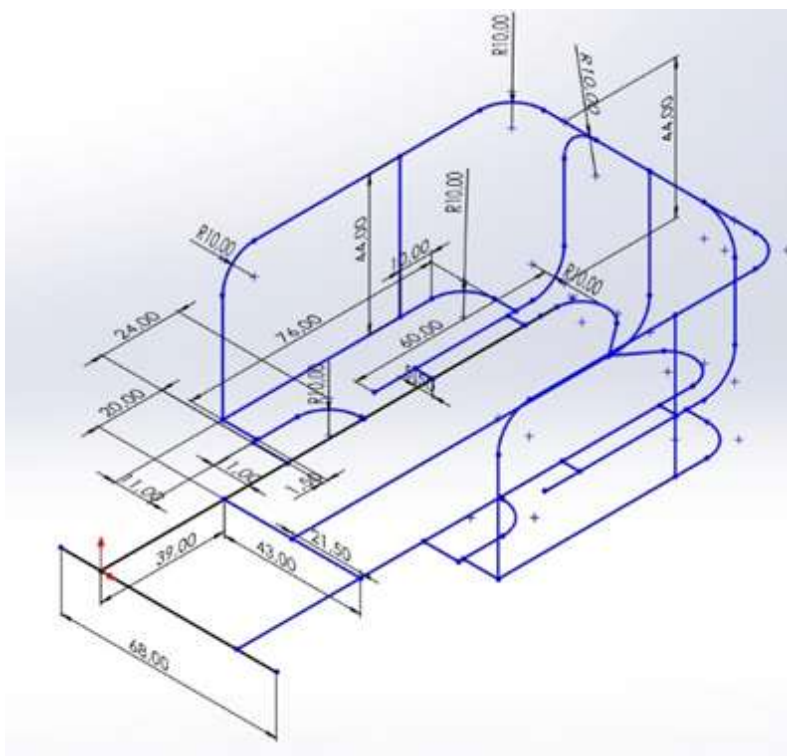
Plano dimensional del chasis elaborado en SolidWorks.
